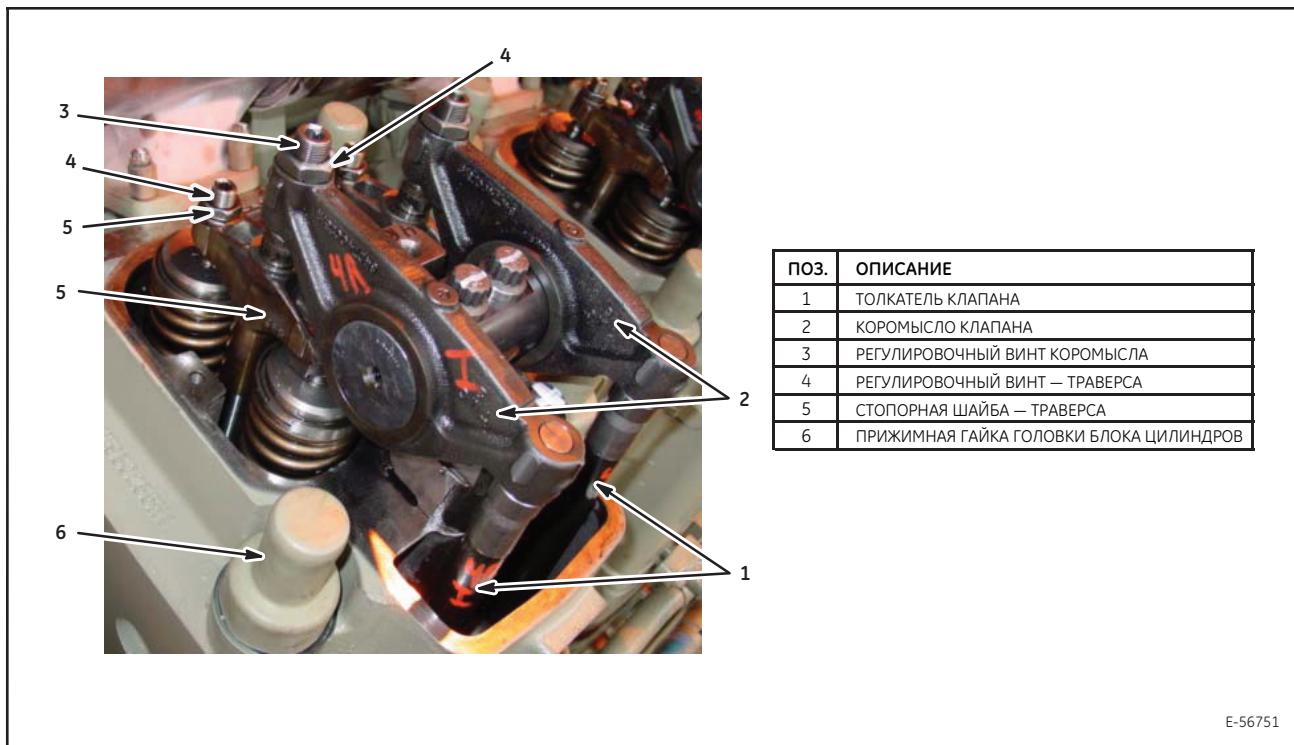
Штифтовая траверса клапана – головка цилиндров без форсунки инжектора
